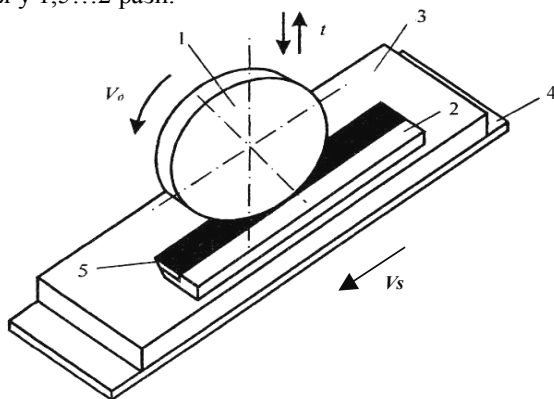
Принципова схема оброблення фрикційним зміцненням плоских поверхонь: 1 – інструмент-диск; 2 - деталь, що обробляється; 3 - магнітна плита; 4 - стіл; 5 - зміцнений шар
